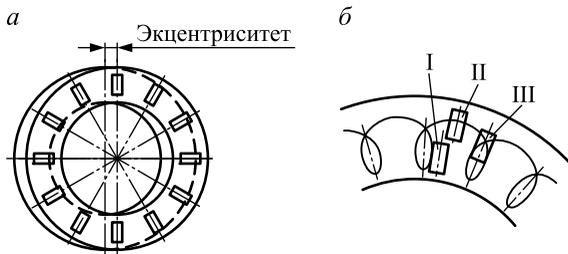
Схема притирки наружной цилиндрической поверхности на станке:
